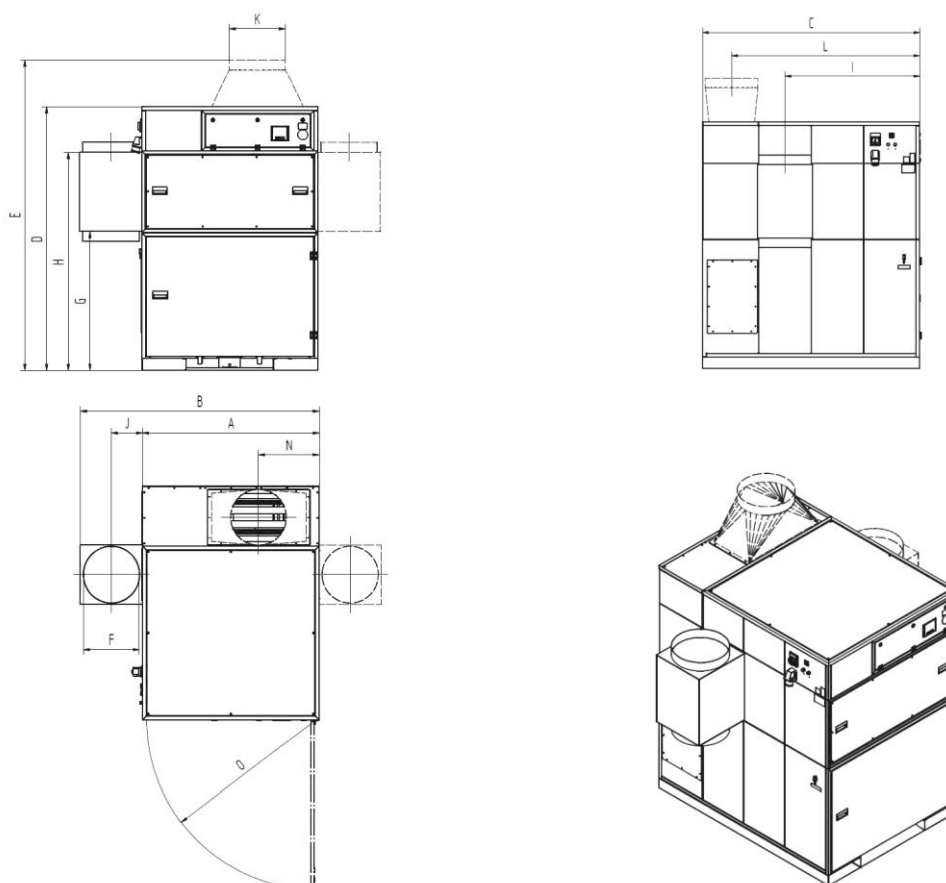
Габаритный чертеж 3740, 324018, 324019
